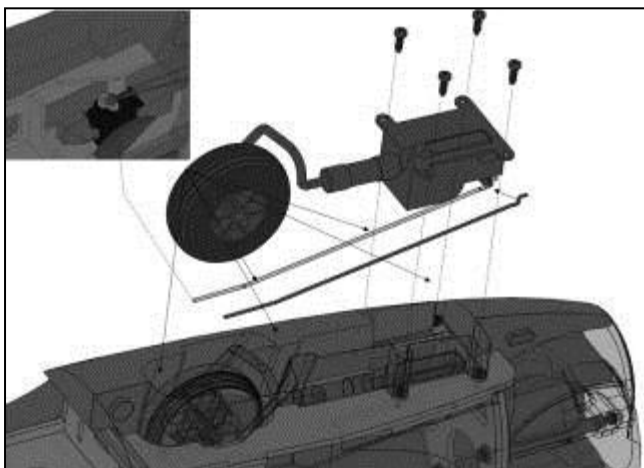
Zur Montage des Servos für das lenkbare Bugrad, die Gestängeaufnahme (Pos 15) innen am Ruderarm verschrauben. Ggfs. Bohrung mit einem geeigneten Bohrer anpassen.
